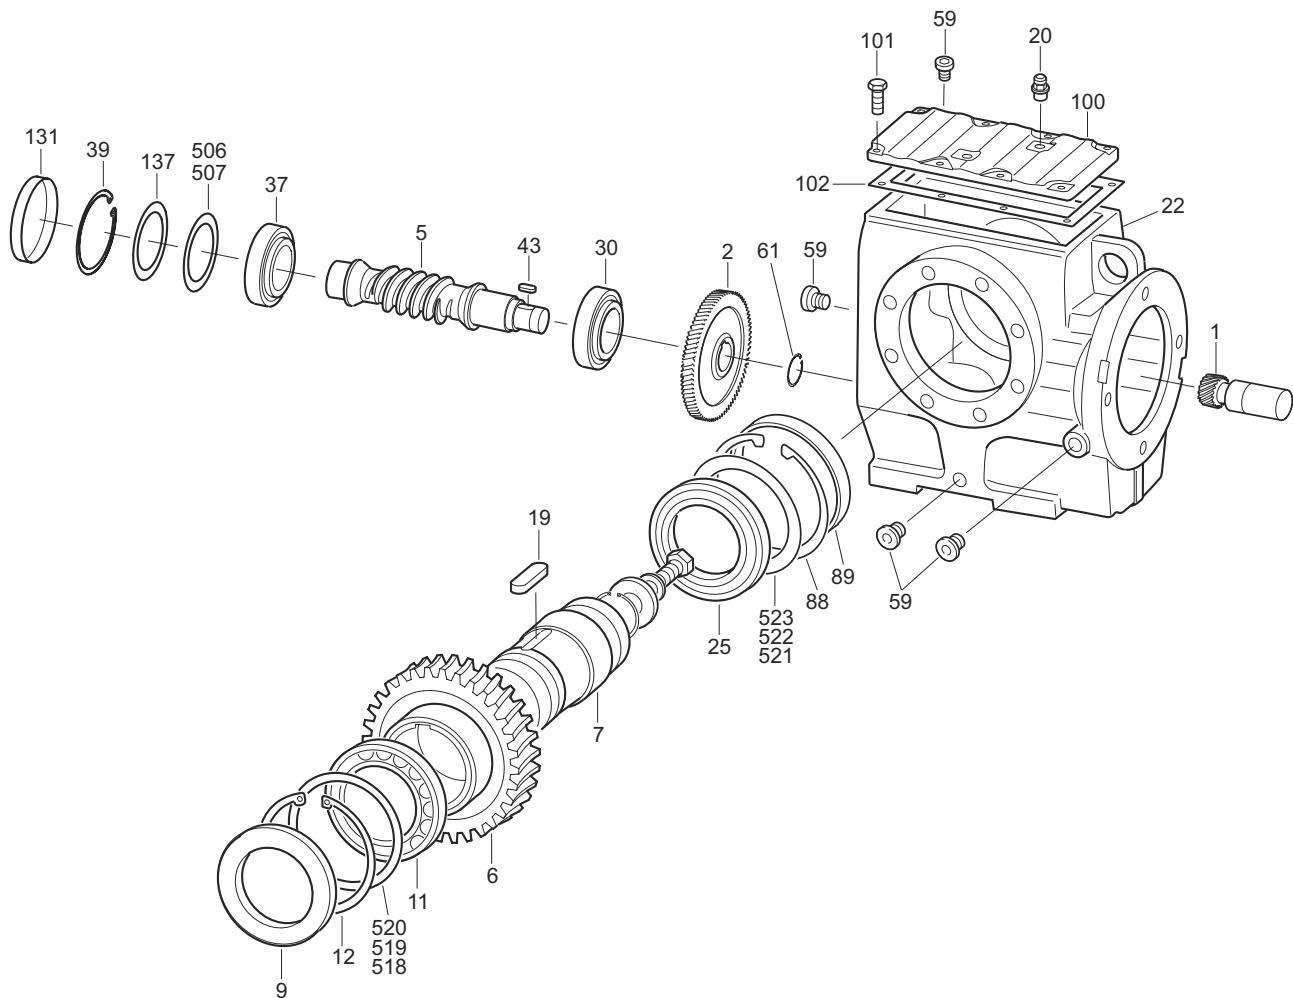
Prinzipieller Aufbau Schneckengetriebe
